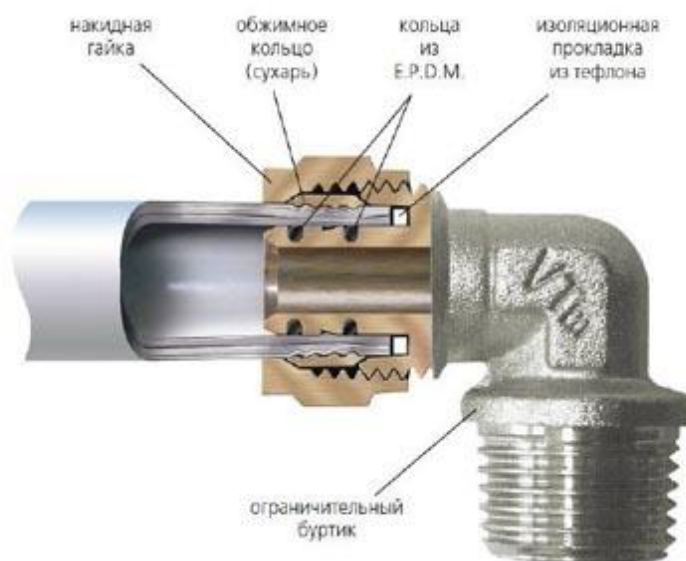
Пресс - фитинг для металлопластиковых труб
